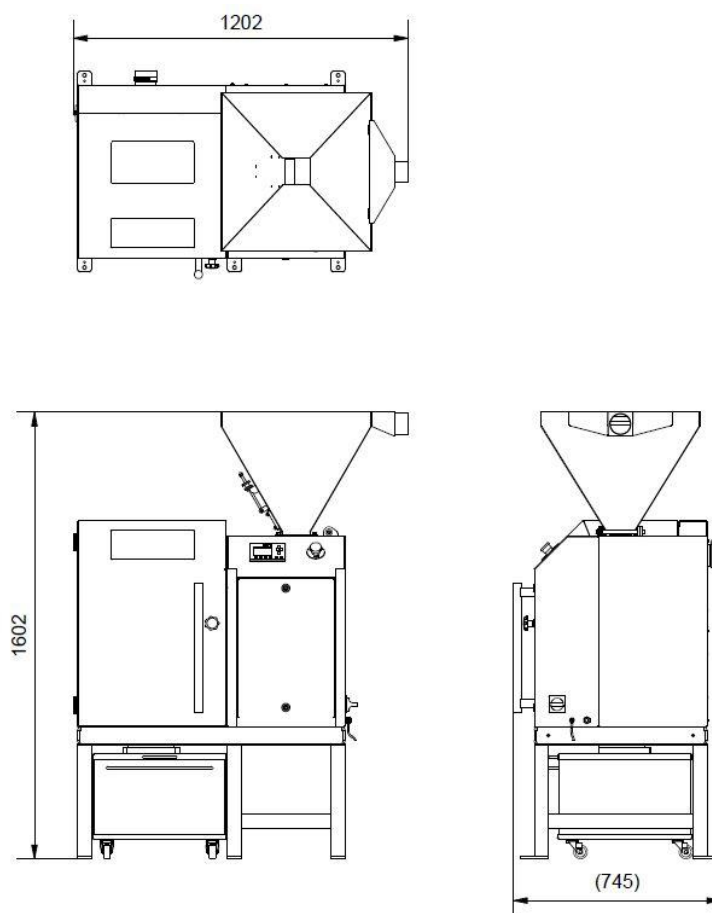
Дверца корпуса закрыта — воронка 60 л
